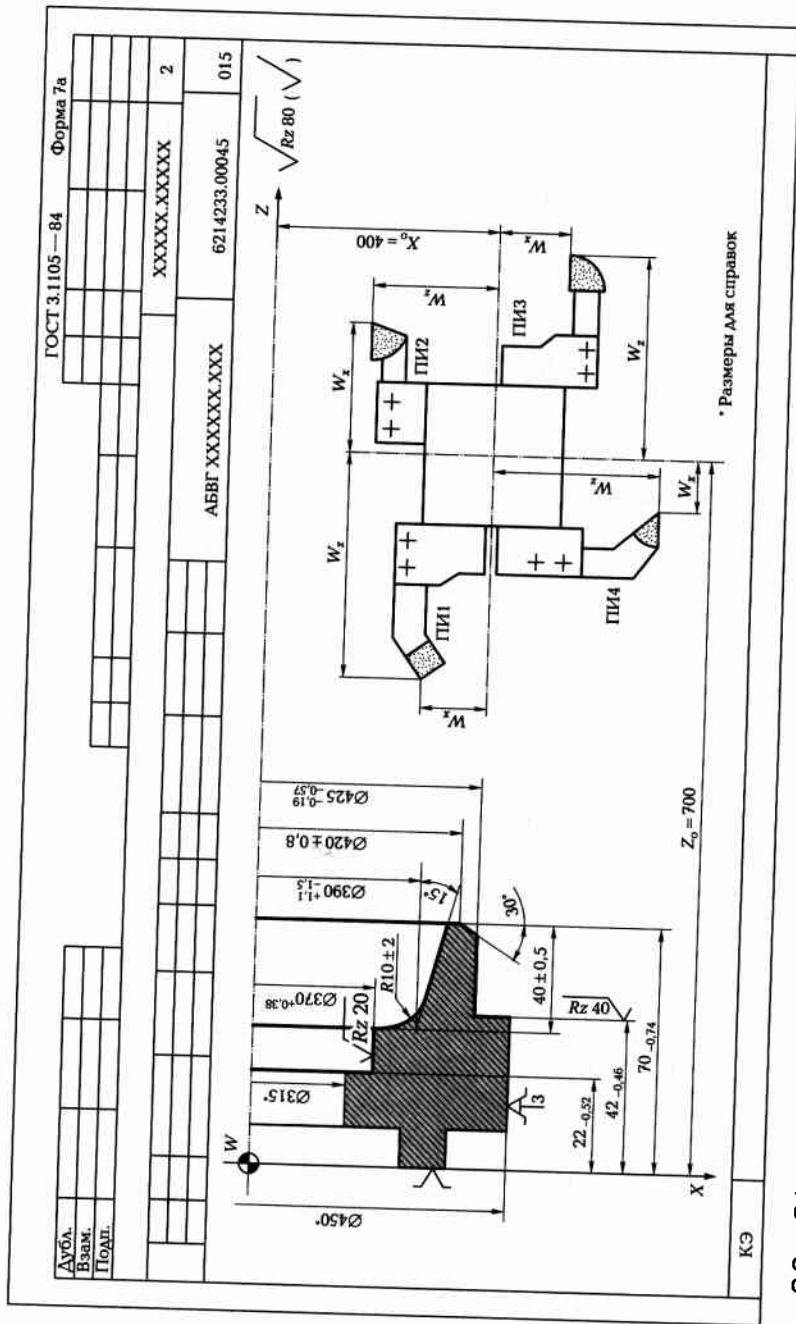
Оформление карты наладки инструмента для станков с ЧПУ
